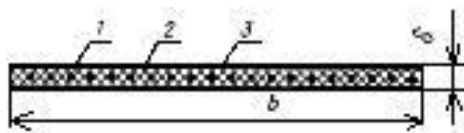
Кордшнуровый прорезиненный ремень:
